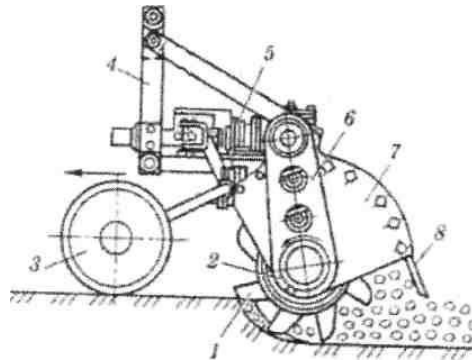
Схема модернізованої фрези: 1 – ніж, 3 – опорне колесо, 2 – барабан, 5 і 6 – редуктори, 4 – навіска, 8 – решітка, 7 – кожух.
